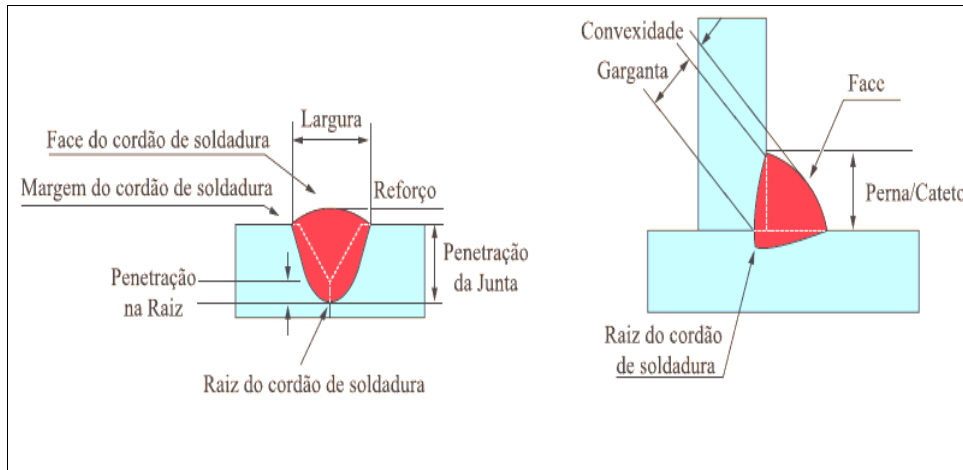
Nomenclatura relacionada com a geometria dos cordões de soldadura
